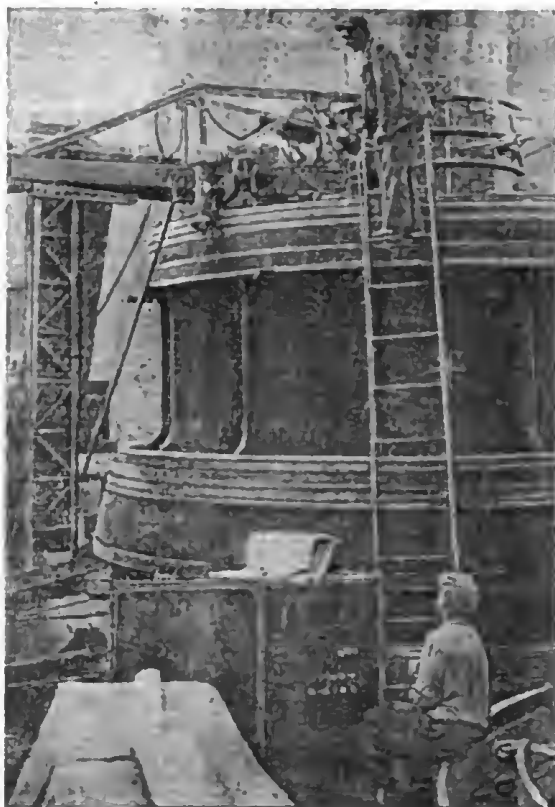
Приспособление для шлифовки обода и лабиринтных колец.
